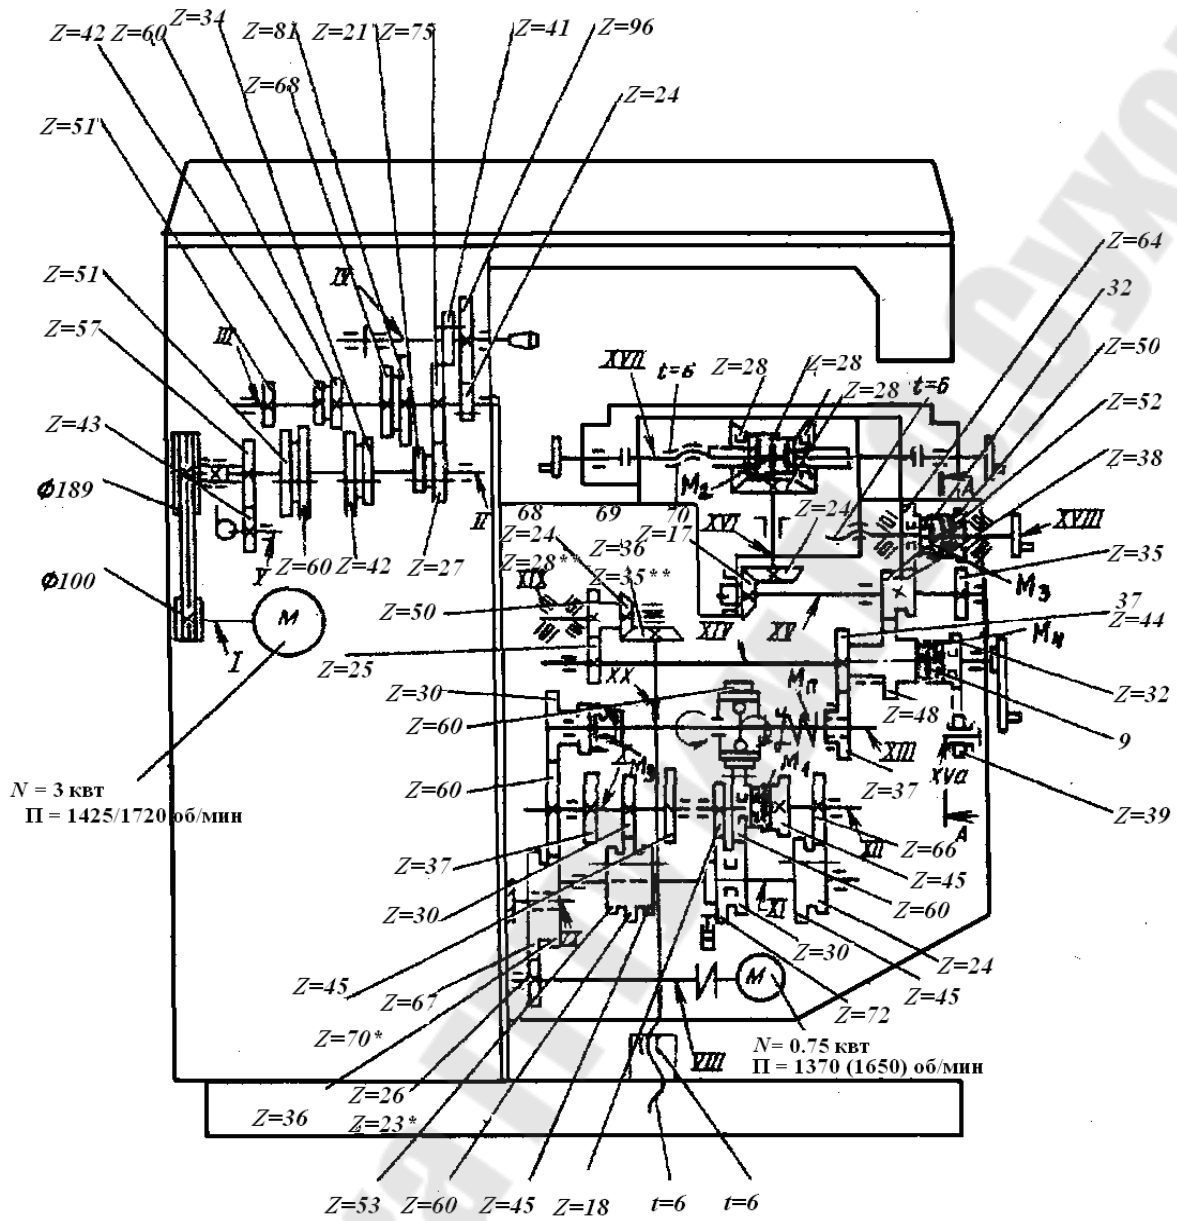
Кинематическая схема горизонтально-фрезерного станка
